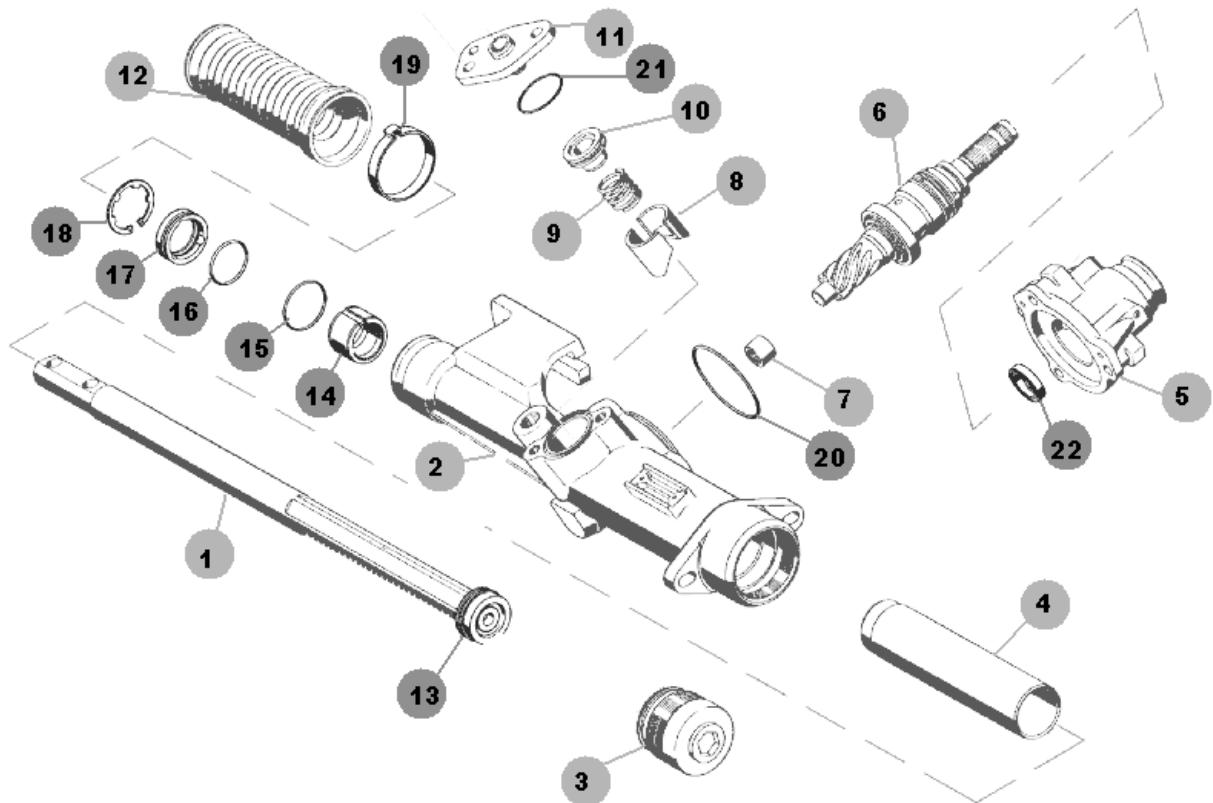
Конструкція механічної рульової рейки 2-й вид:
